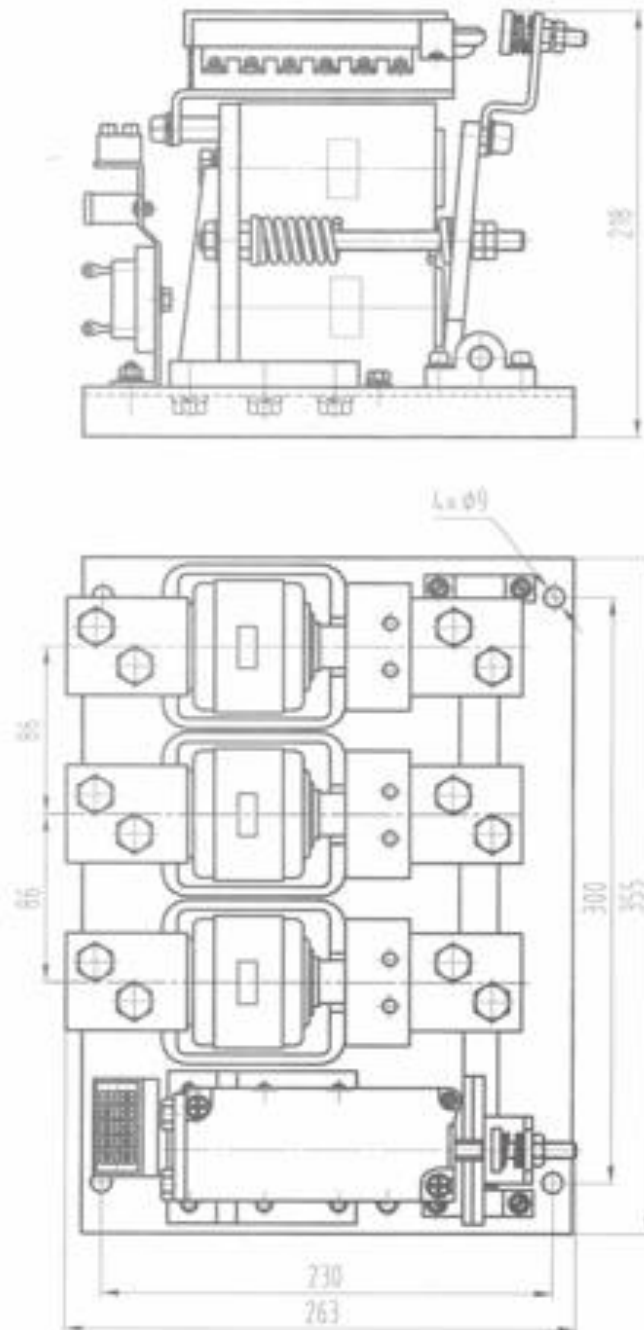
SOSKJ5-250/1140 desenho e dimensional de instalação
